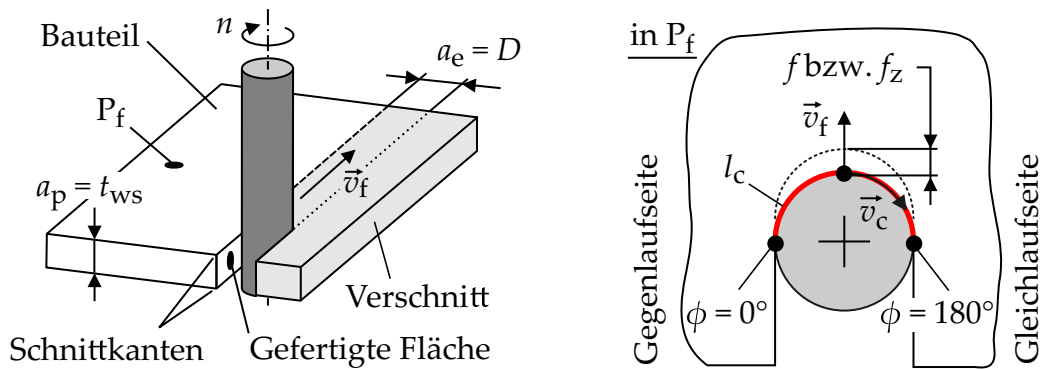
Eingriffskinematik bei der Zerspänung mit zylinderförmigen Schaftwerkzeugen
